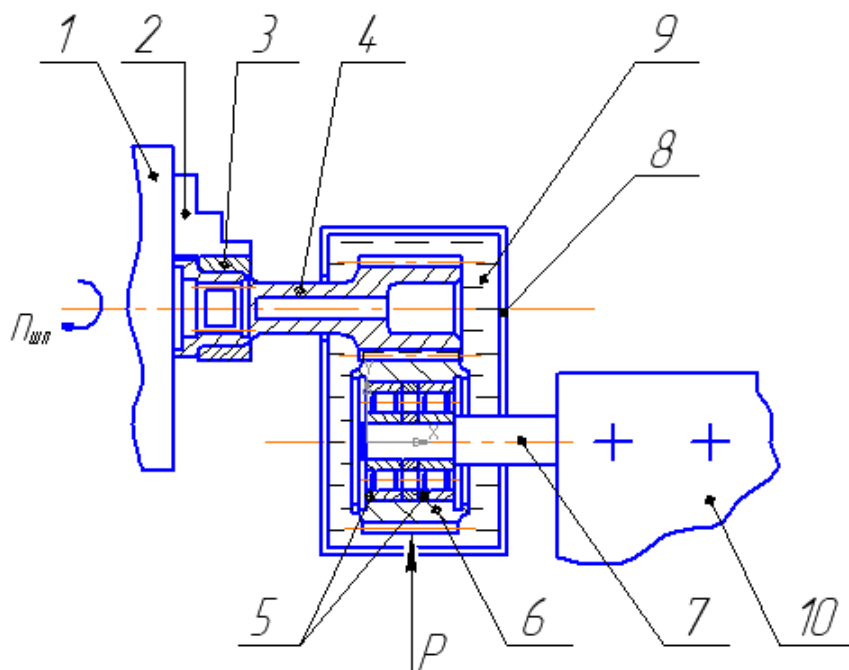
Схема обработки зубчатых колёс. Наружное зацепление:
